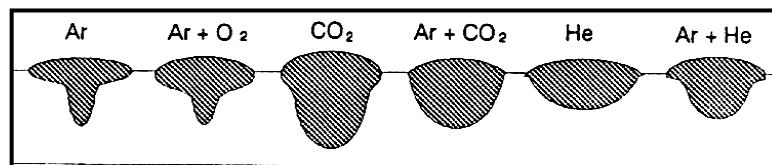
Perfil de cordões de solda utilizando diferentes gases (MARQUES, 1991).
